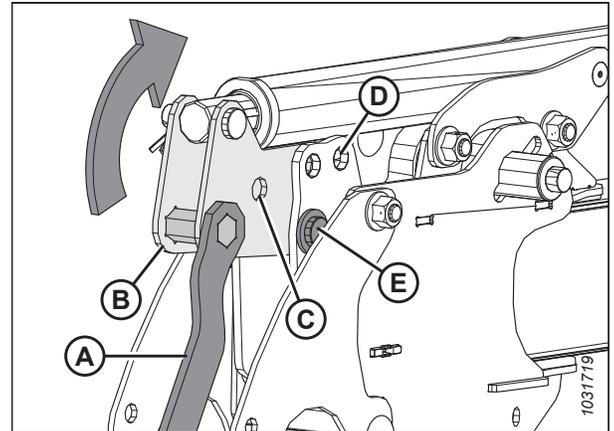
Cilindro del braccio destro – Posizione avanzata
